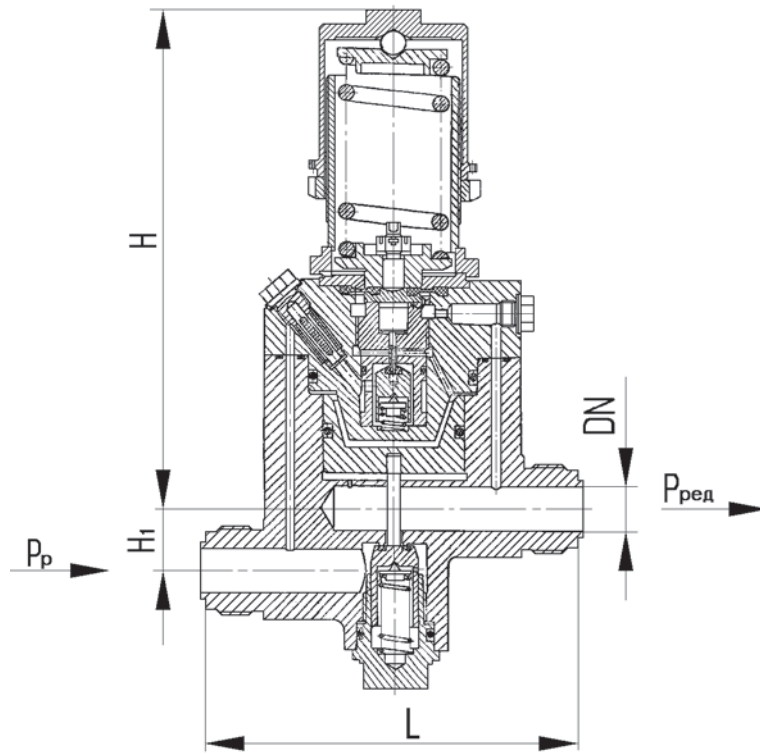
Клапан редукционный проходной штуцерный
